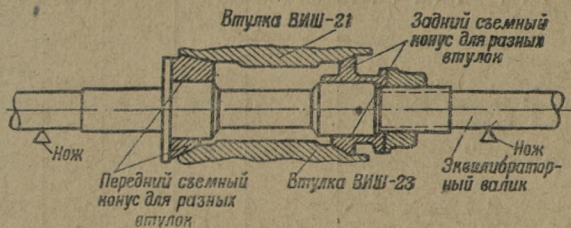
Схема закрепления винта для балансировки на эквilibраторном валике
